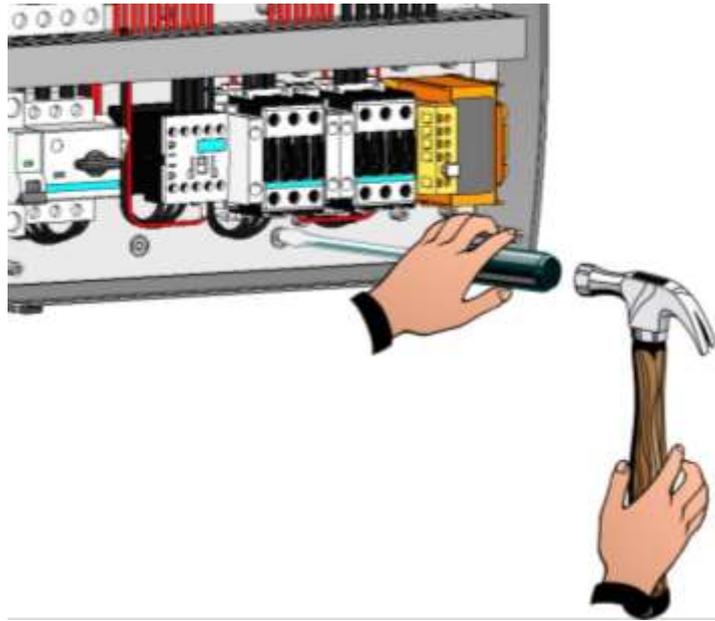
Die 4 Befestigungsschrauben des Vorderteils des Schaltkastens abschrauben.
